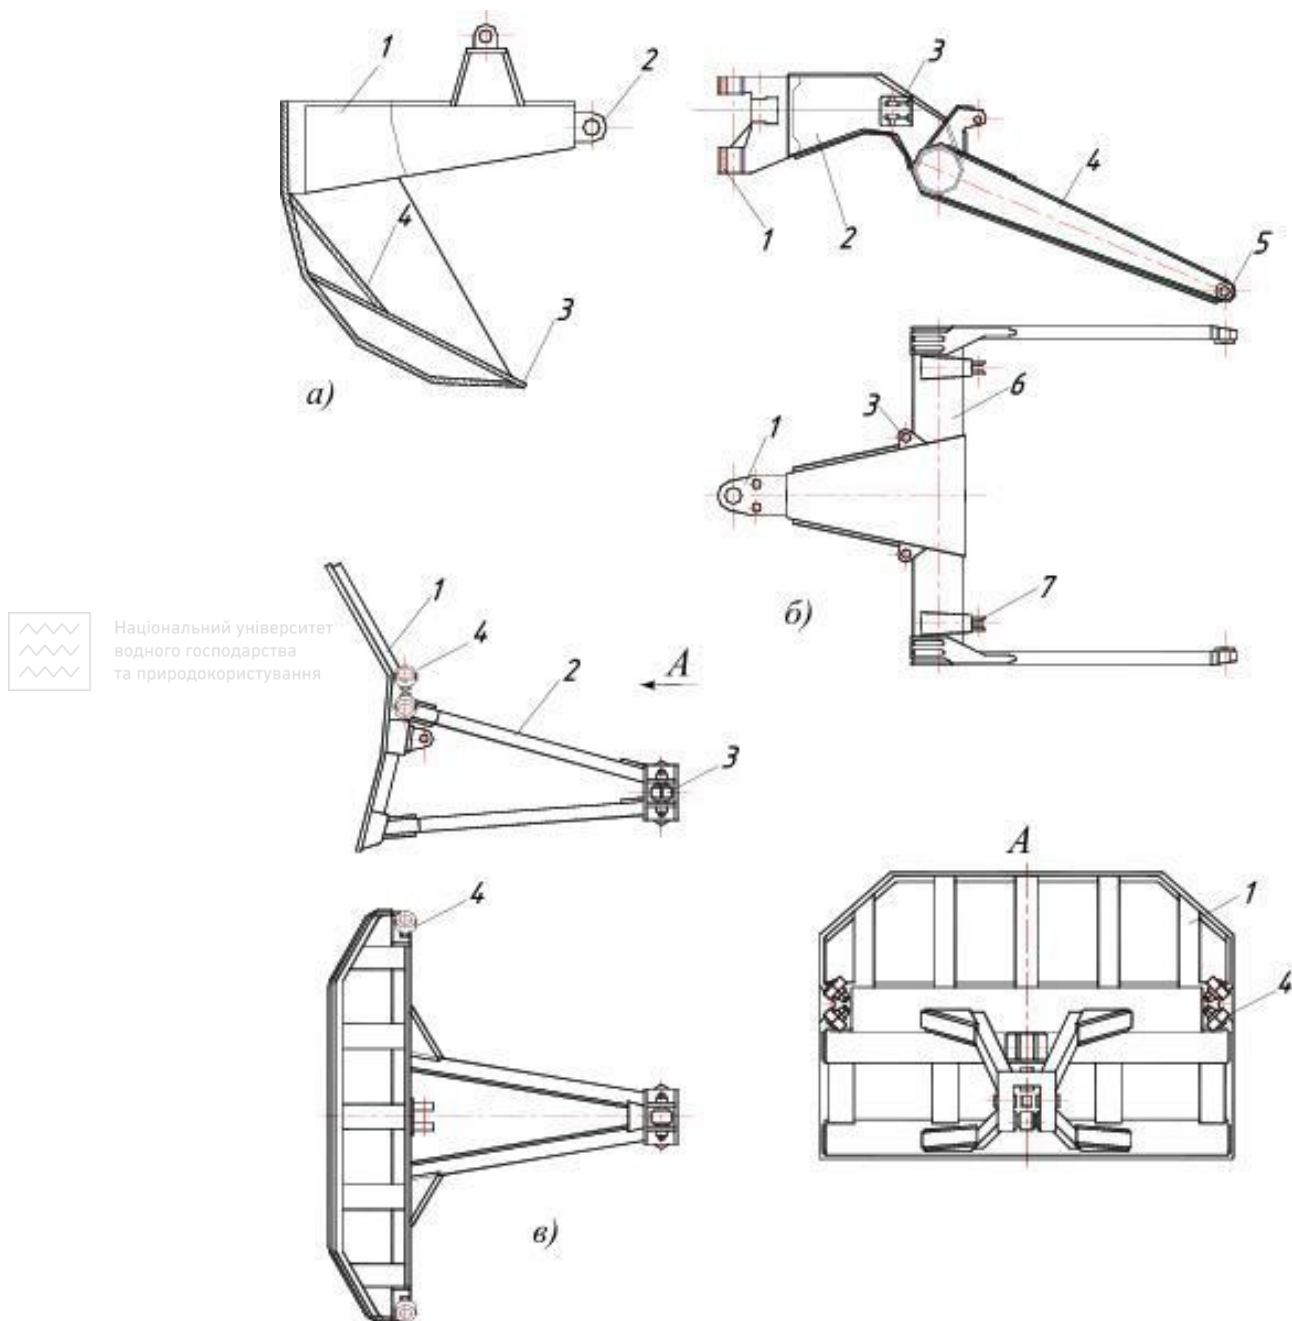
Конструктивні схеми елементів робочого обладнання скрепера:
